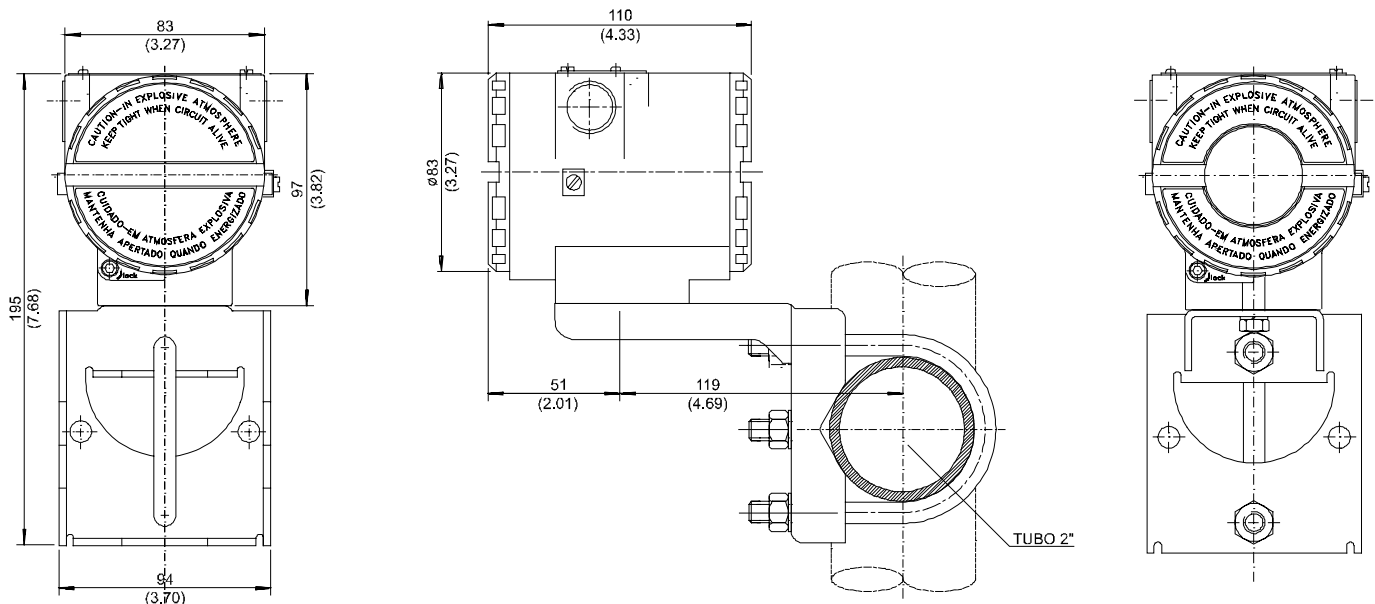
Posições de Montagem e Desenho Dimensional
